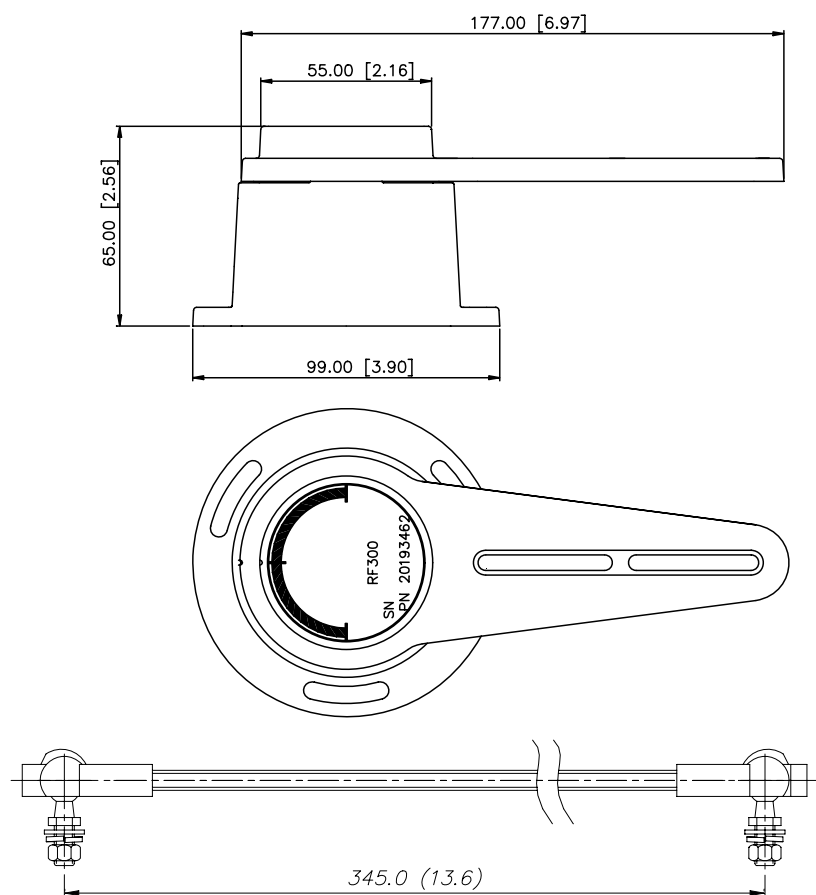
Dimensions du capteur d'angle de barre RF300
